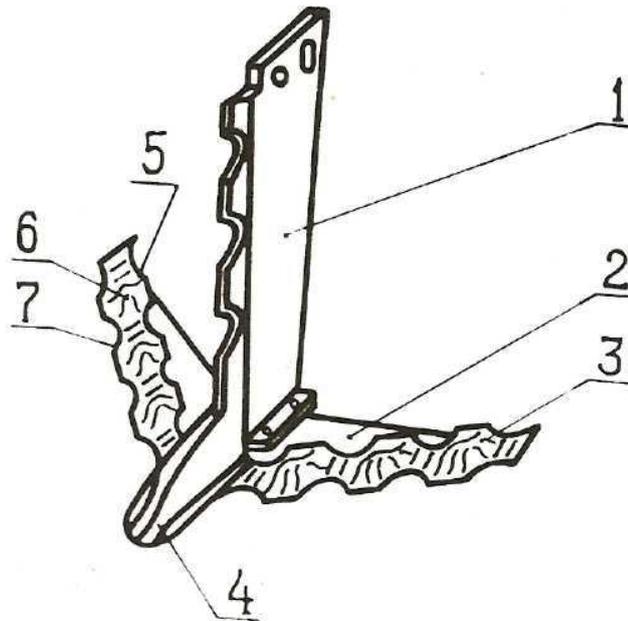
Зубчатий плоскорізний робочий орган
